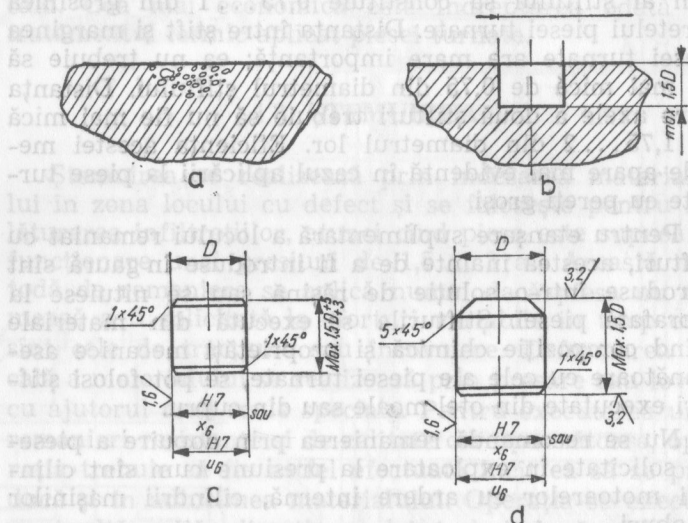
Pregătirea locului cu defect în vederea dopuirii: a — defectul în piesa turnată; b — locul cu defect pregătit pentru remaniere; c — forma și dimensiunile dopului introdus prin presare; d — forma și dimensiunile dopului ce se sudează pentru remaniere prin dopuire.
